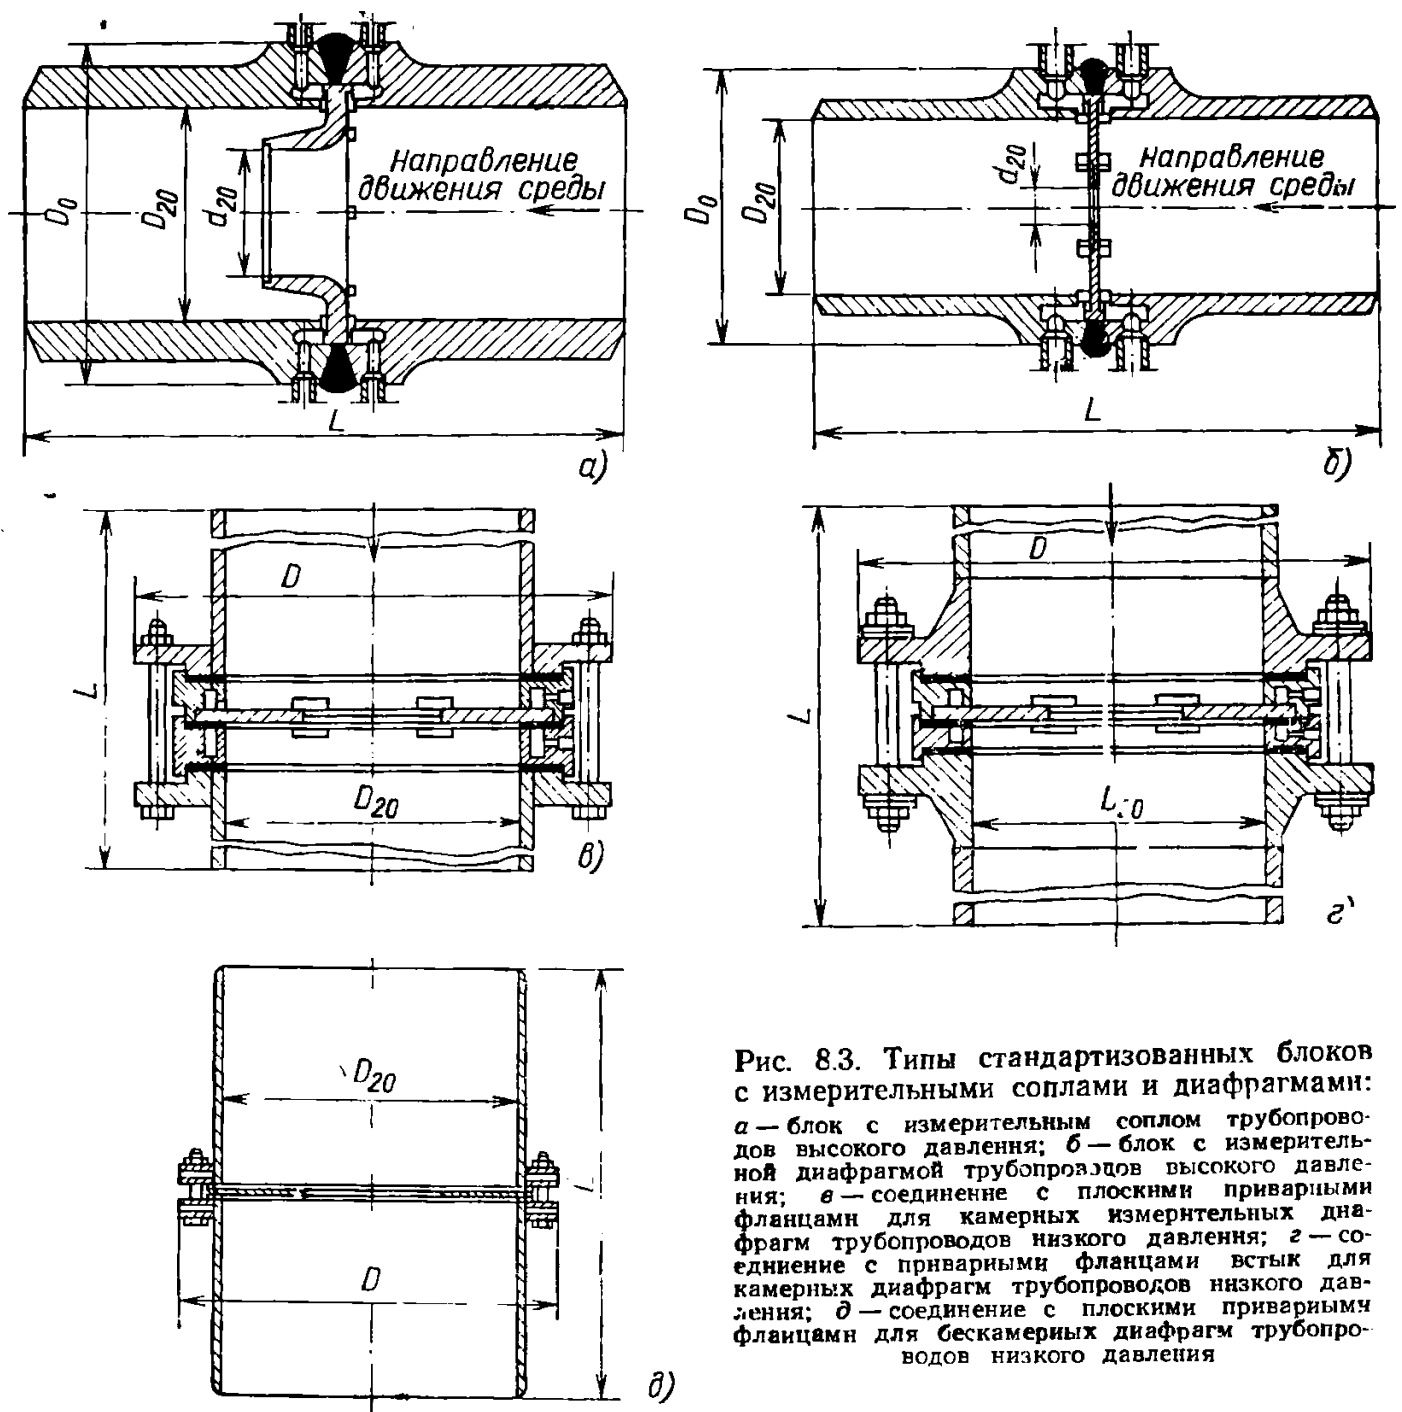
Типы стандартизованных блоков с измерительными соплами и диафрагмами: а — блок с измерительным соплом трубопроводов высокого давления; б — блок с измерительной диафрагмой трубопроводов высокого давления; в — соединение с плоскими приварными фланцами для камерных измерительных диафрагм трубопроводов низкого давления; г — соединение с приварными фланцами встык для камерных диафрагм трубопроводов низкого давления; г' — соединение с плоскими приварными фланцами для бескамерных диафрагм трубопроводов низкого давления
